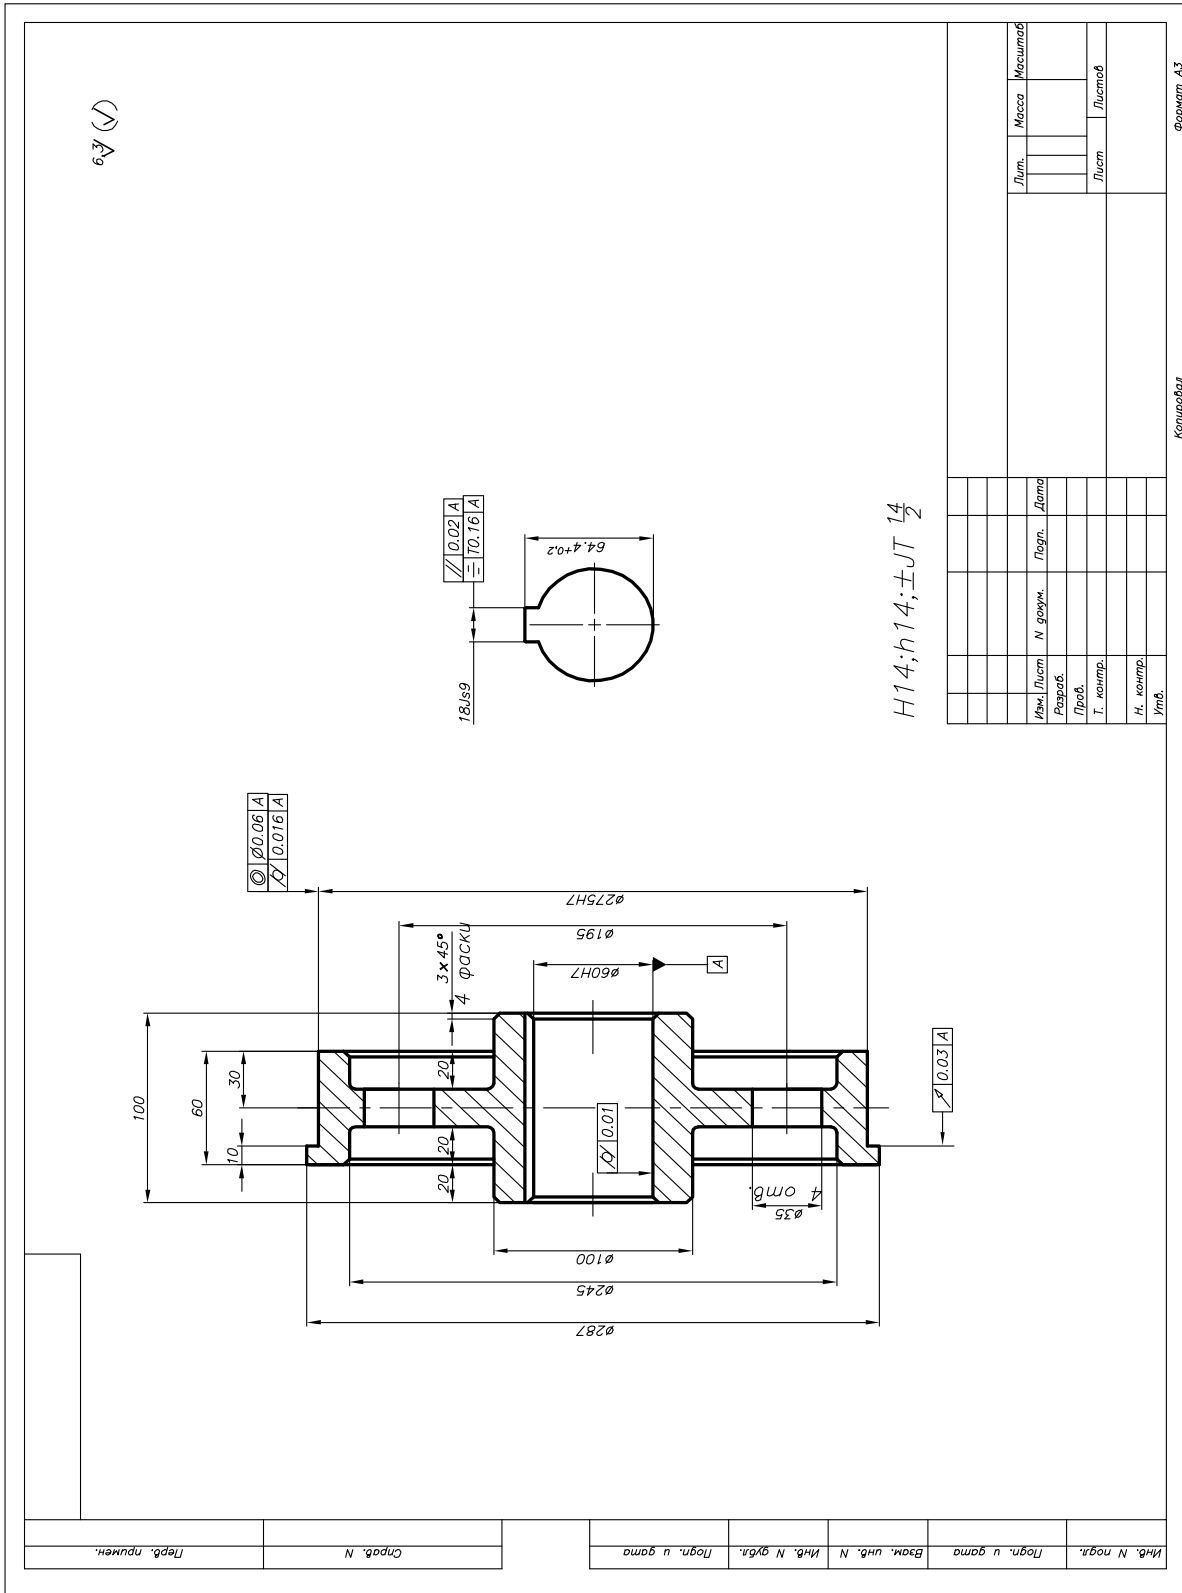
Рабочий чертеж колеса червячного (сборочный чертеж)
